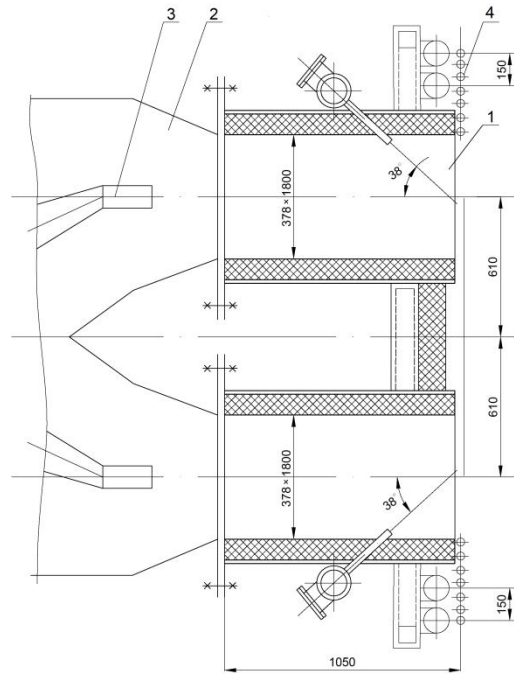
Схема пылегазовой горелки котла БКЗ-210-140Ф
